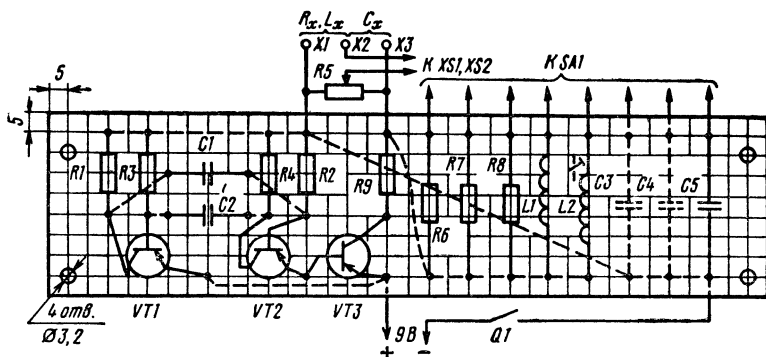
Разметка монтажной платы и схема соединений деталей на ней
